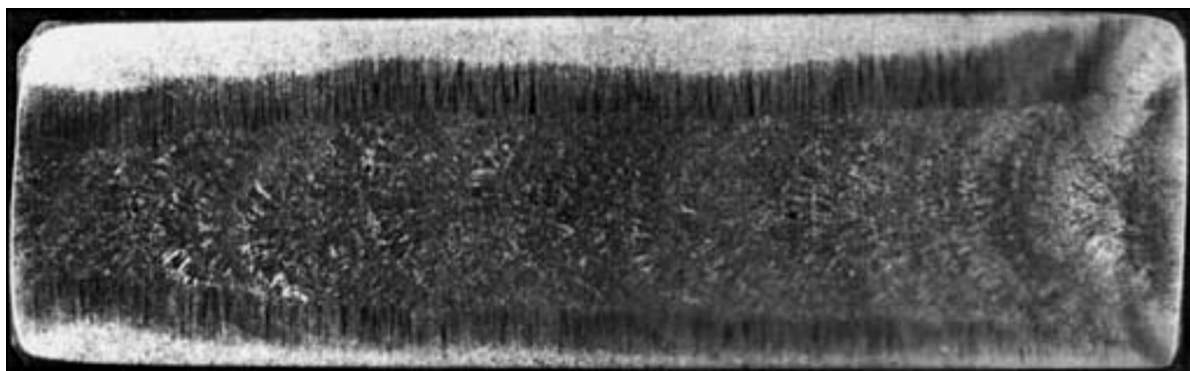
Макроструктура ($\times 1,7$) металла шва сварного соединения стали 10ГН2МФА, полученного ААрДС в узкую разделку кромок в смеси 70 % He + 30 % Ar с использованием сварочной проволоки Св-08Г1НМА
